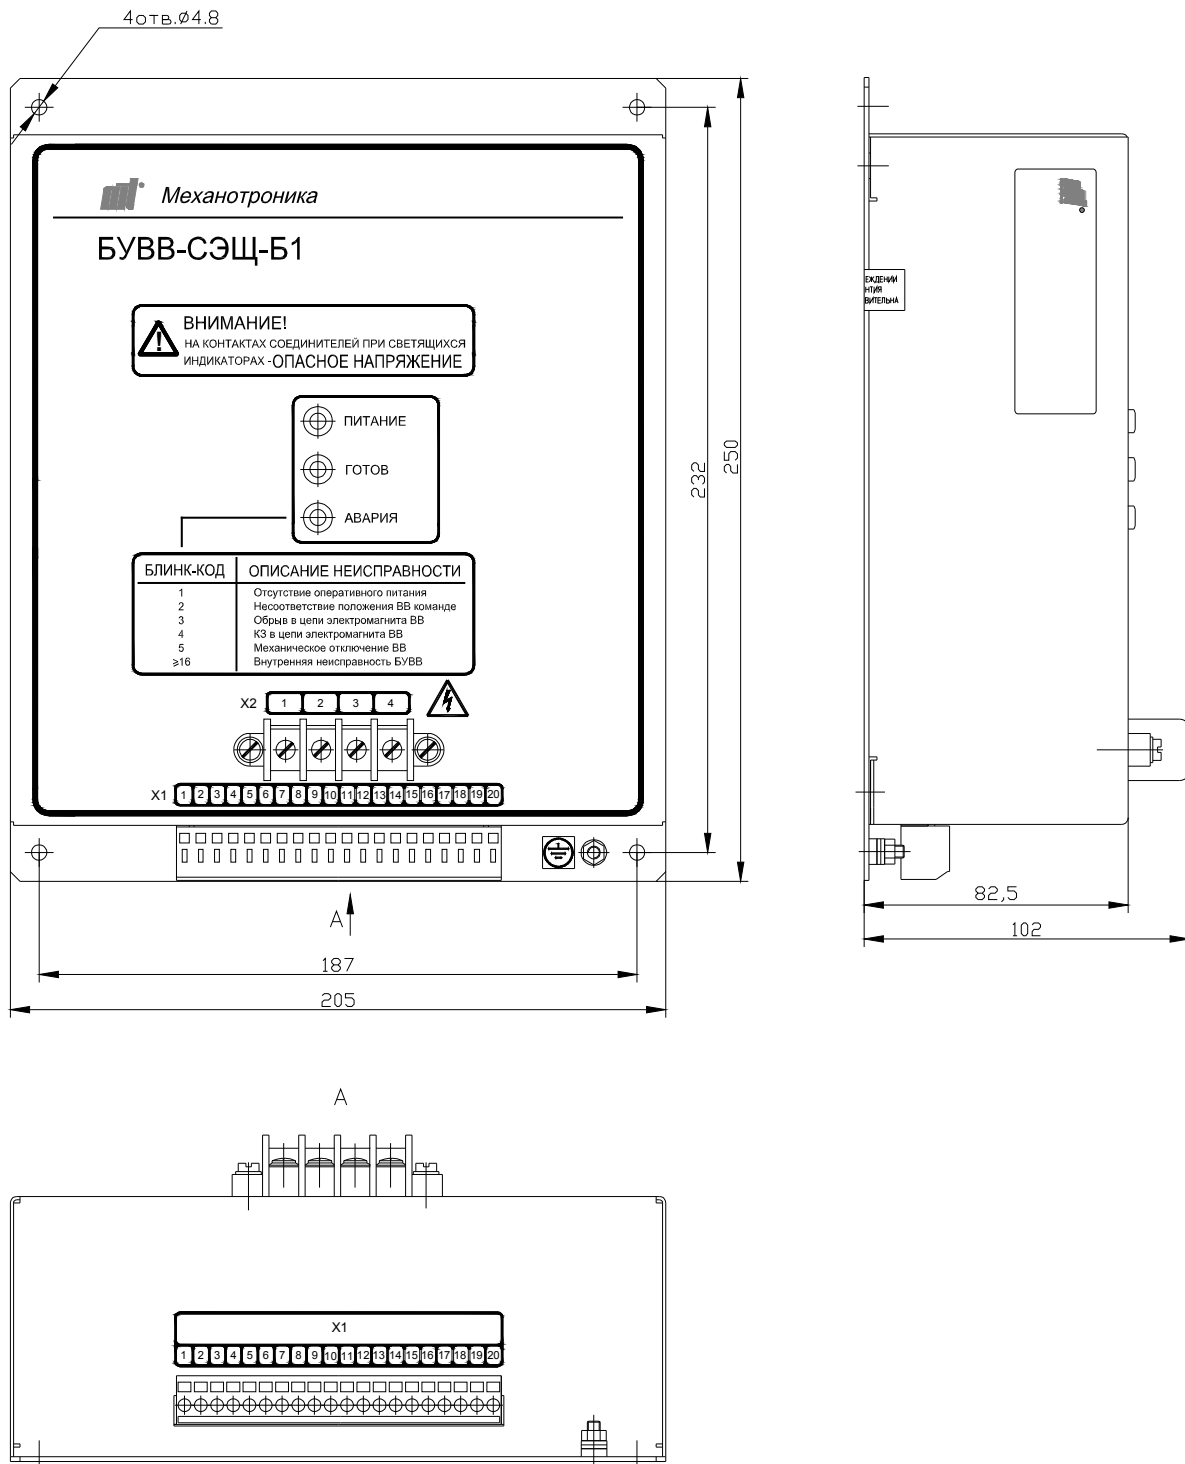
Вид блока ДИВГ.648228.102, габаритные и установочные размеры
